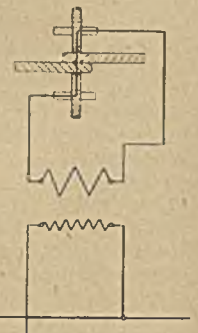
Widerstandsschweißung mittels transformierten Wechselstromes: Rollen-Nahtschweißung.
